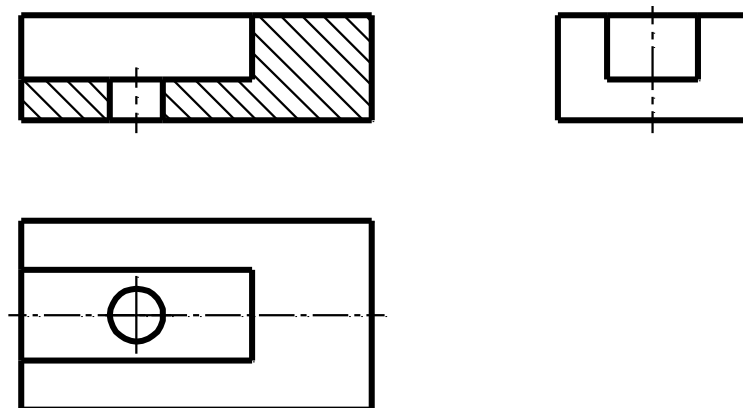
Фронтальный разрез, вид сверху и вид слева
